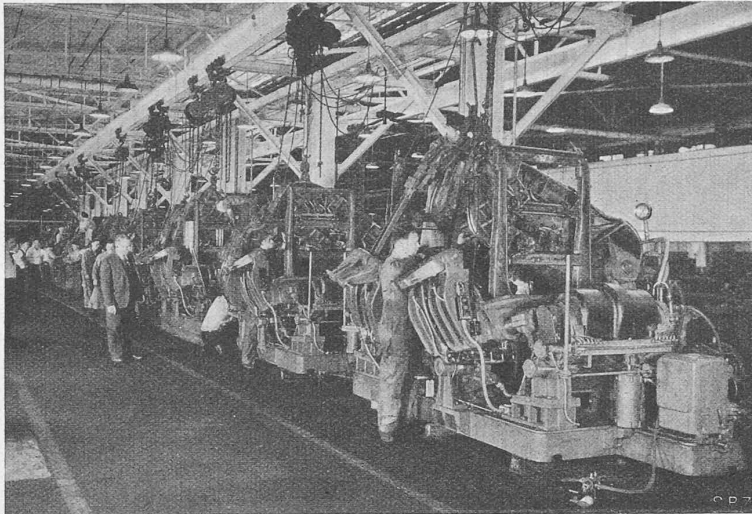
300 kVA-Karosserie-Schweissmaschinen in einer Automobilfabrik
